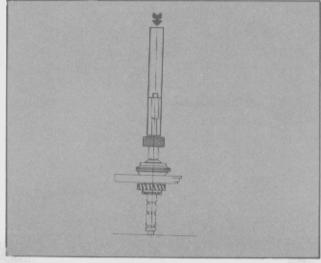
Colocación del engranaje sinfín del velocímetro.
